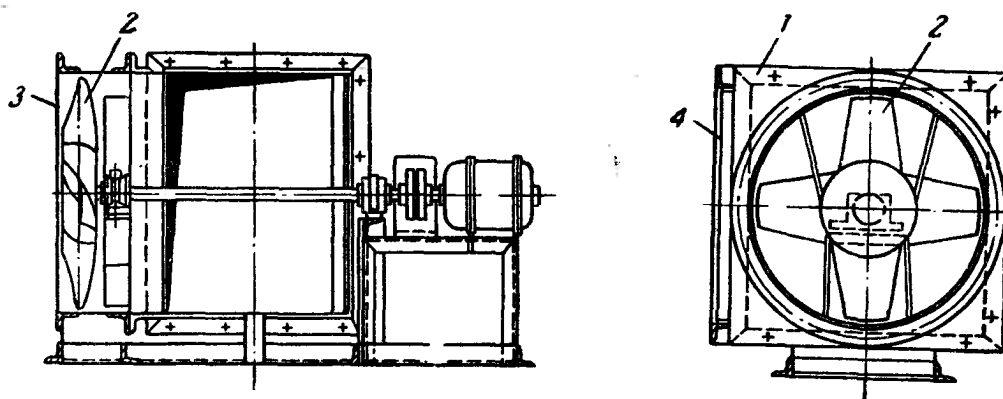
Осьовий вентилятор ЦАГІ: 1 - кожух; 2 – лопатеве колесо (пропелер); 3 – всмоктувальний патрубок; 4 – нагнітальний патрубок.
